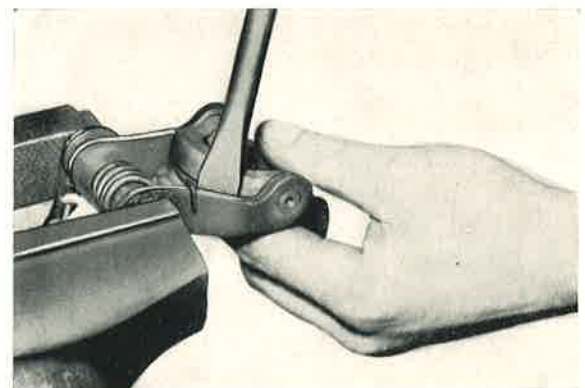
Der Kupplungshebel kann mittels Schraubenzieher zur Herausnahme des Ringes aufgebogen werden.
